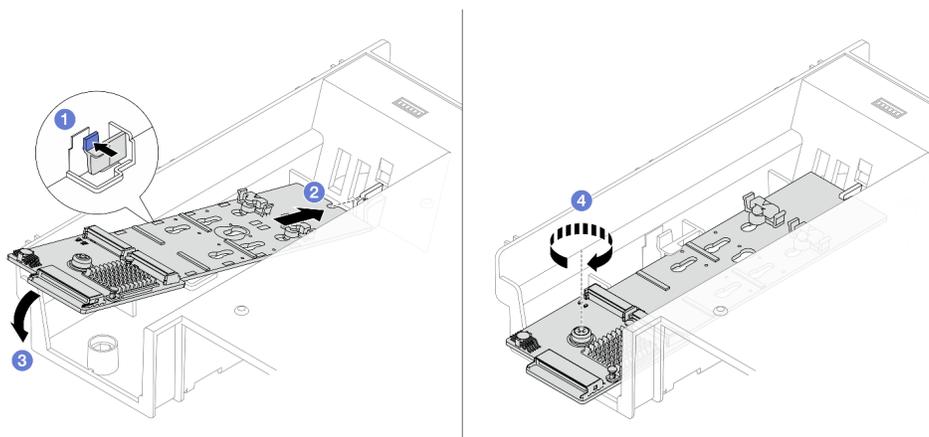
Installation du fond de panier M.2 sur la grille d'aération
